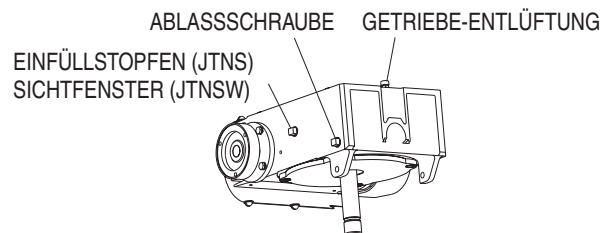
Getriebe-Einfüllstopfen/Sichtfenster
